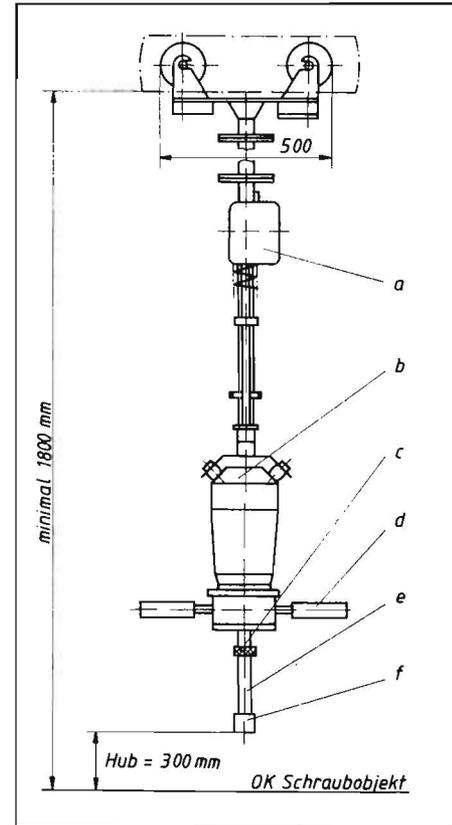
Hydraulischer Einspindelschrauber; a Aufhängung mit Federzug, b Schrauberelement, c Schnellwechsler für Spindel mit Steckfuß, d Haltegriffe mit Druckknopfsteuer, e Spindel, f Steckfuß entsprechend Schraubobjekt
